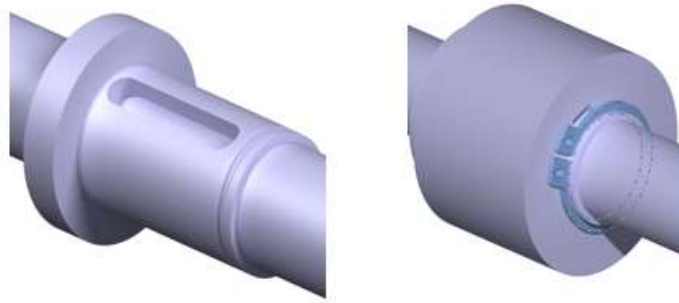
Welle (li. ohne Zahnrad, re. mit Zahnrad und Sicherungsring)
